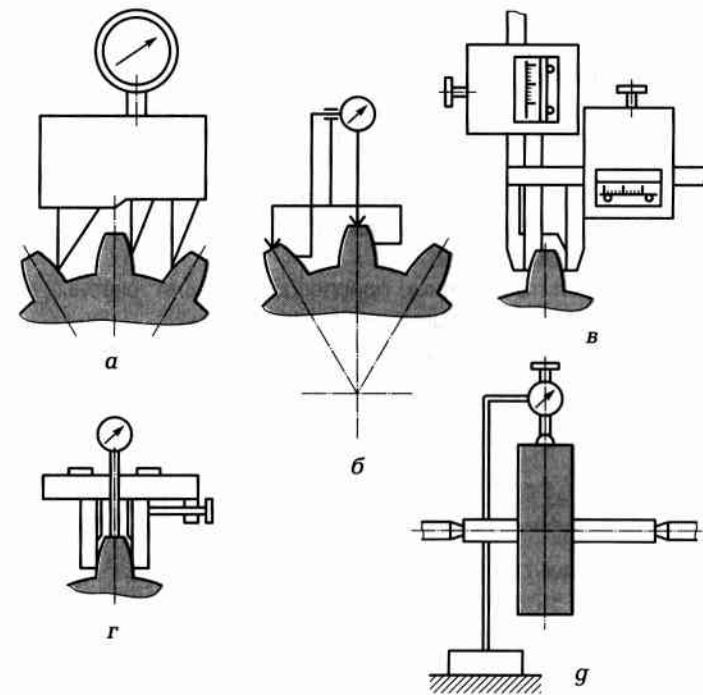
Схемы контроля зубчатых колес (а—д)
